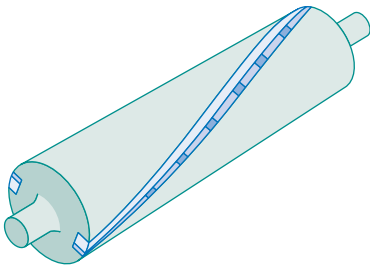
Schéma du porte-outil « hélicoïdal » - *Diagram of a "helical" tool holder
